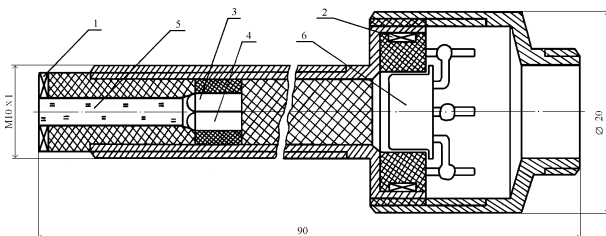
Сборочный чертёж первичного комбинированного первичного преобразователя:
